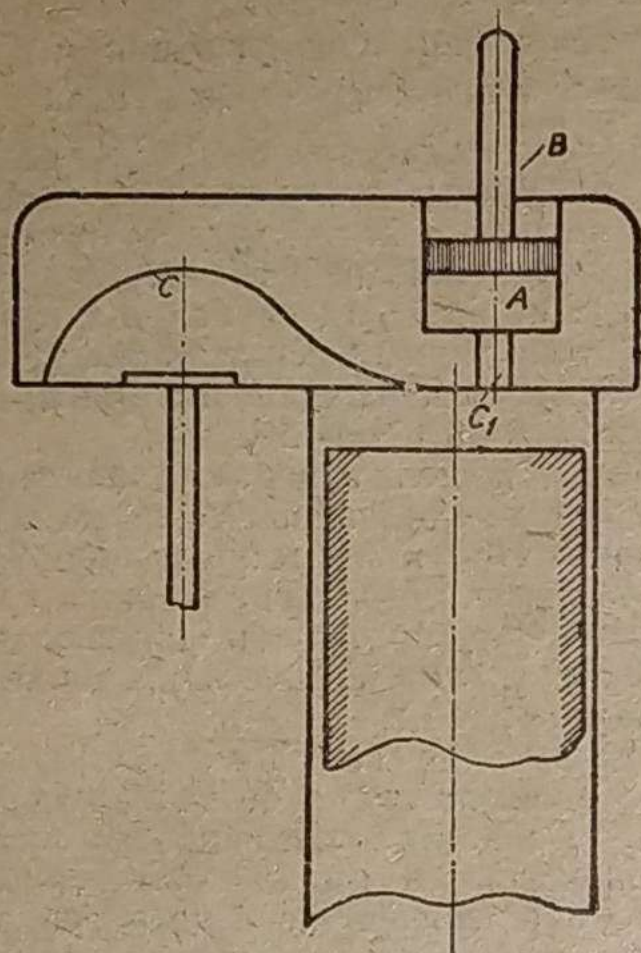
Схема головки двигателя с переменной степенью сжатия. А—добавочная камера, В—поршень для измерения объема сжатия, С—канал, соединяющий добавочную камеру с рабочим цилиндром.
